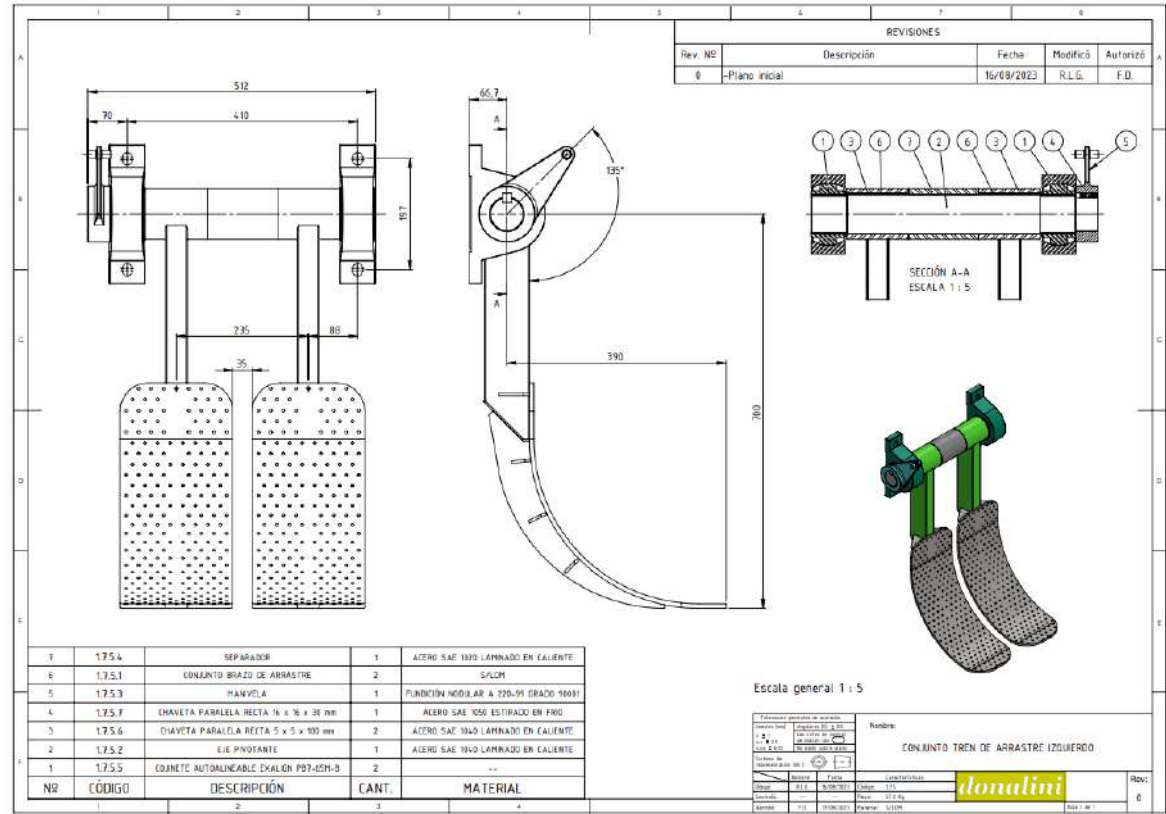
” Plano de Conjunto de Tren de Arrastre”
